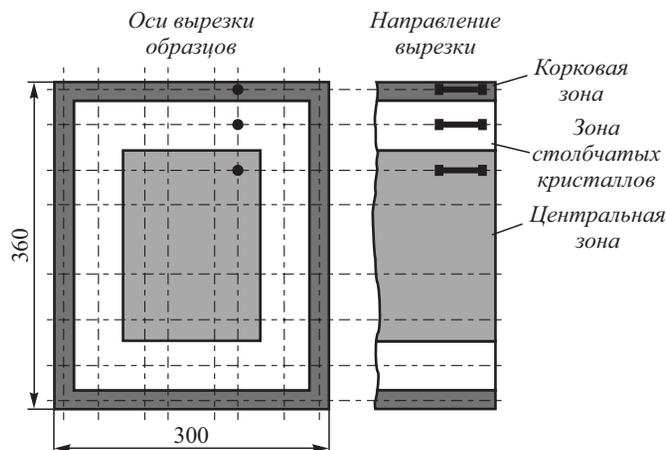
Схема вырезки образцов из зон НЛЗ рельсовой стали
